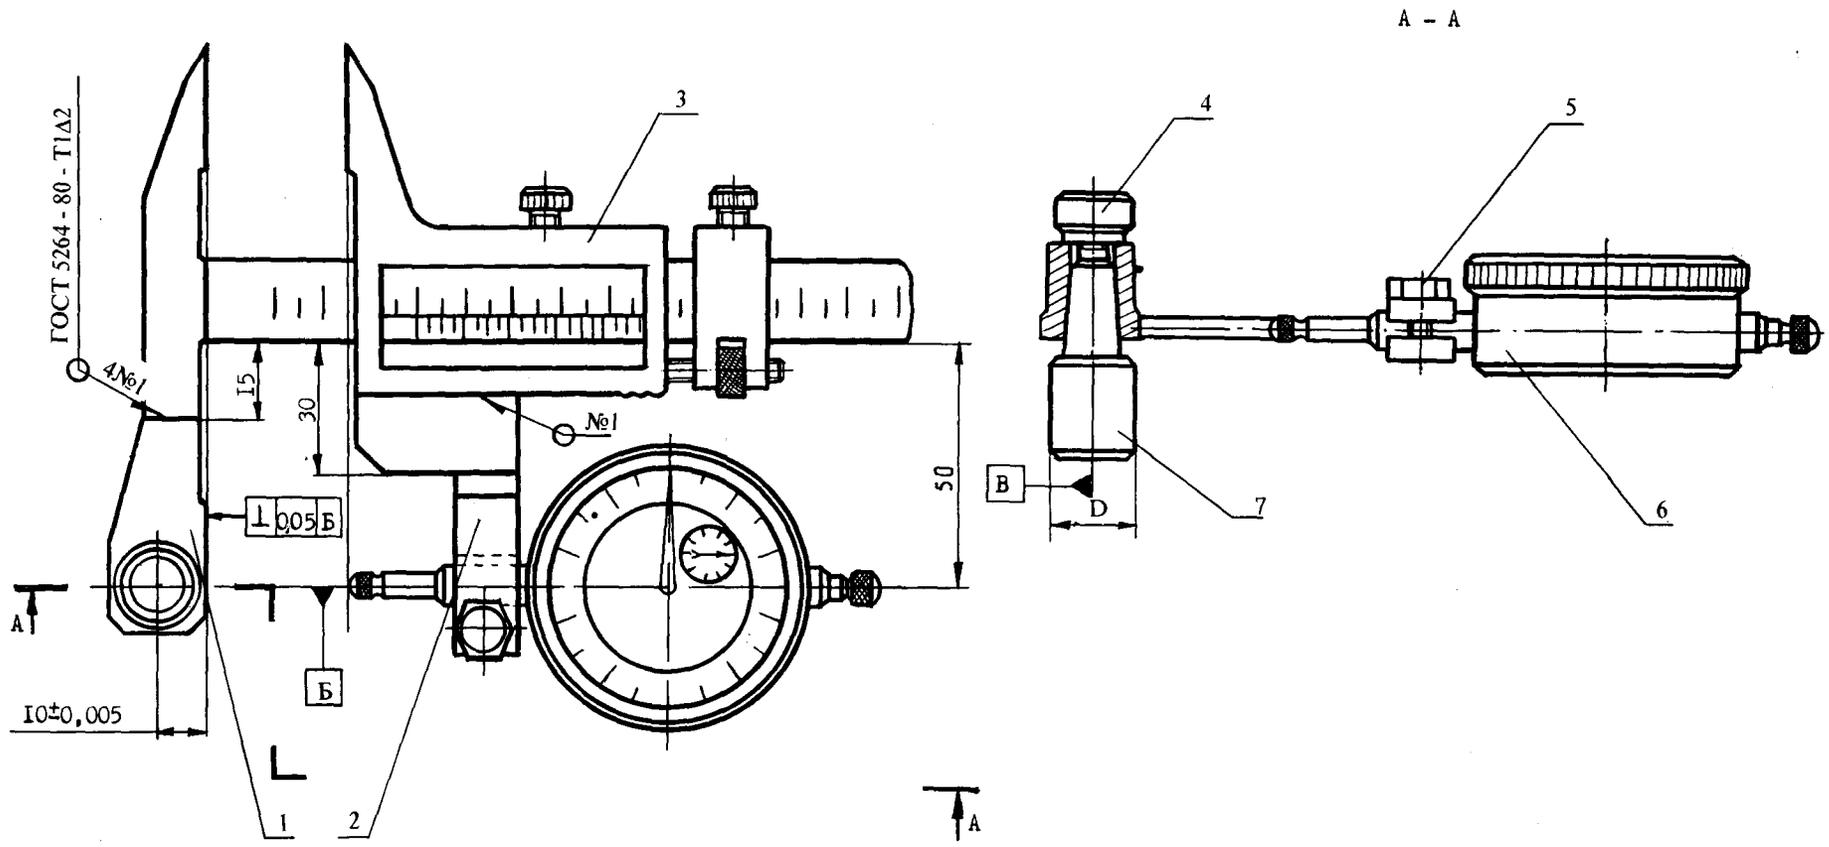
Приспособление для контроля угла подъема и смещения витков у плоских резьбонакатных плашек:
